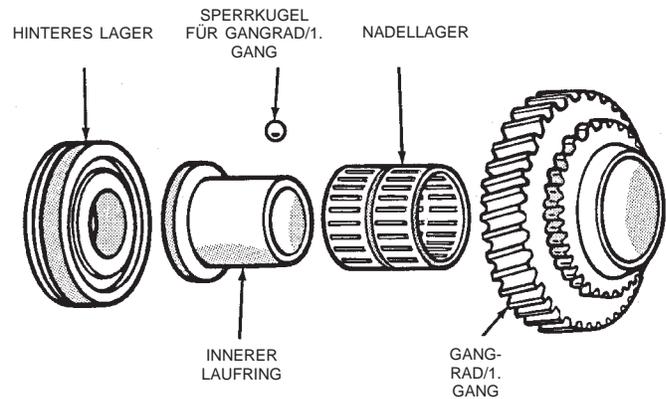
Sperrkugel des inneren Laufrings, Gangrad/1. Gang einbauen
